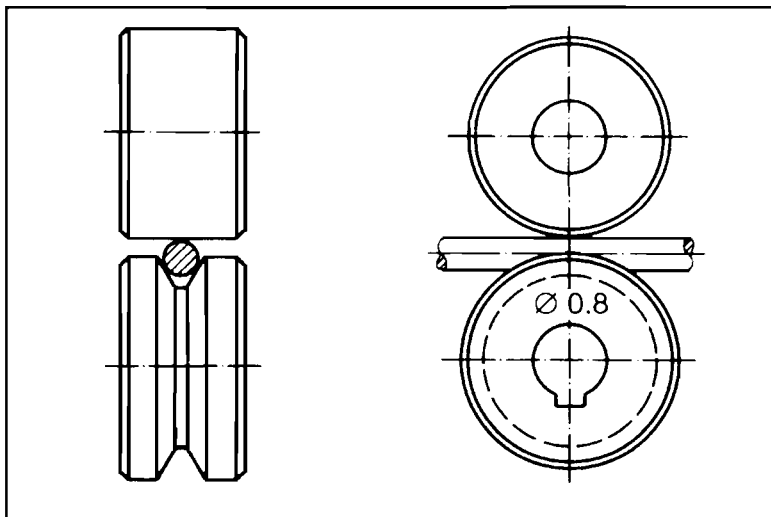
RODILLOS PARA EL SOLDEO MIG/MAG
